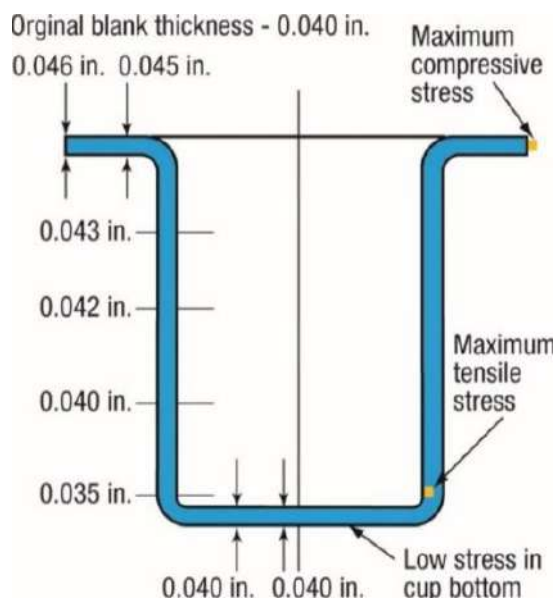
Схема НДС при глибокому витягуванні листової заготовки [6]
